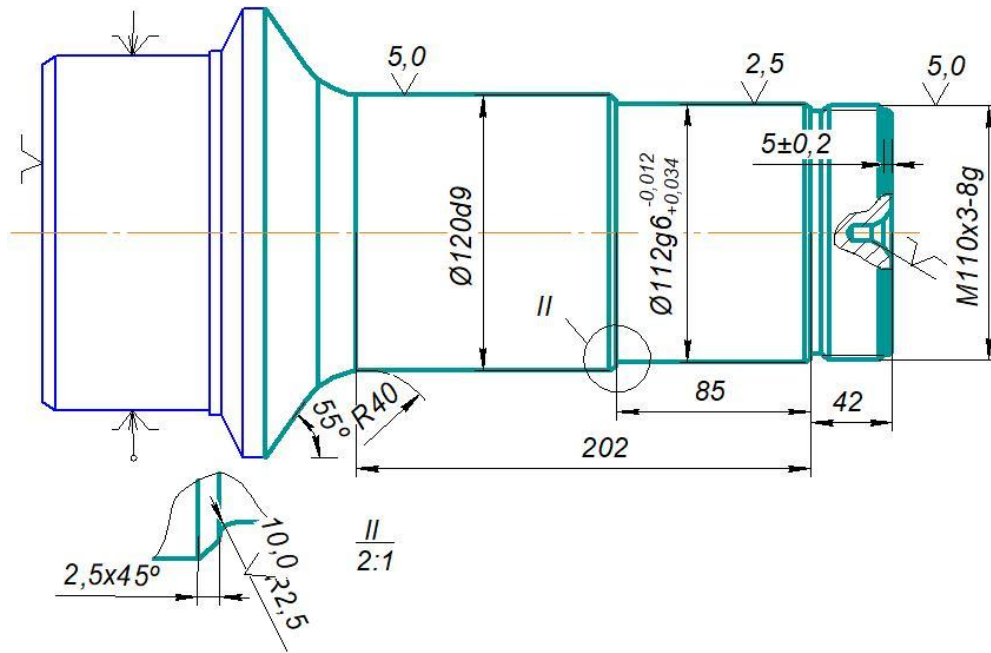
Обробка поверхні Ø120d9 деталі
